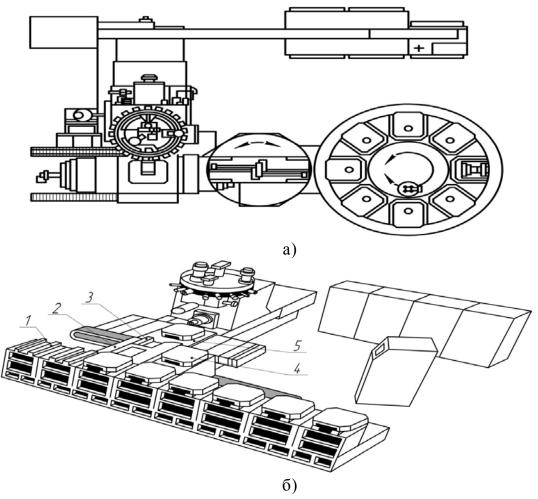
Пристаночные накопители приспособлений-спутников для гибких производственных систем (ГПС): 1- магазин; 2- тележка-оператор; 3,5- позиции; 4- стол
